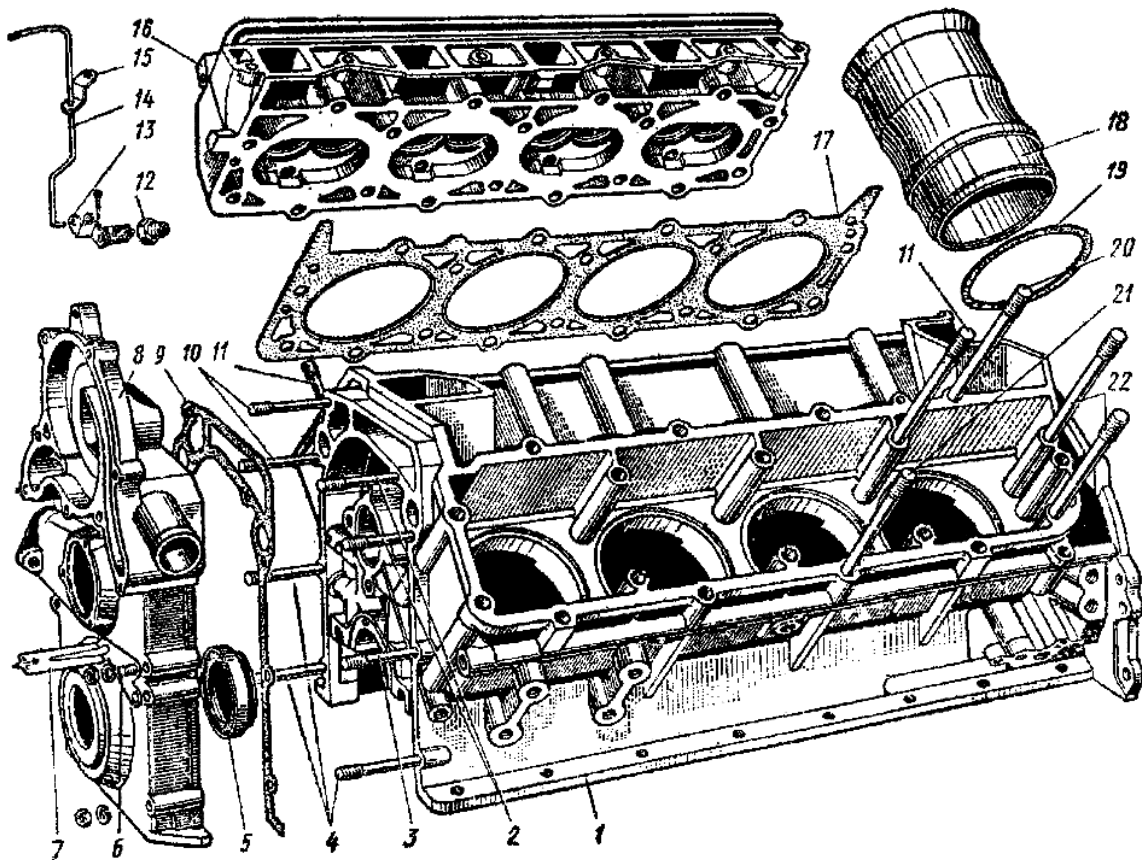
Блок и головка цилиндров двигателя ЗМЗ-53А
